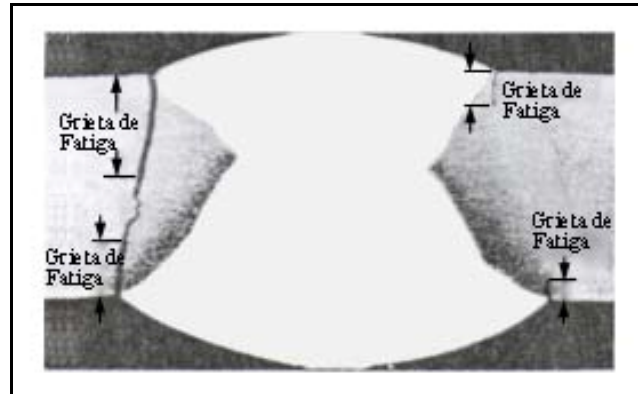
Grietas por fatiga junto a una soldadura longitudinal de una tubería.
